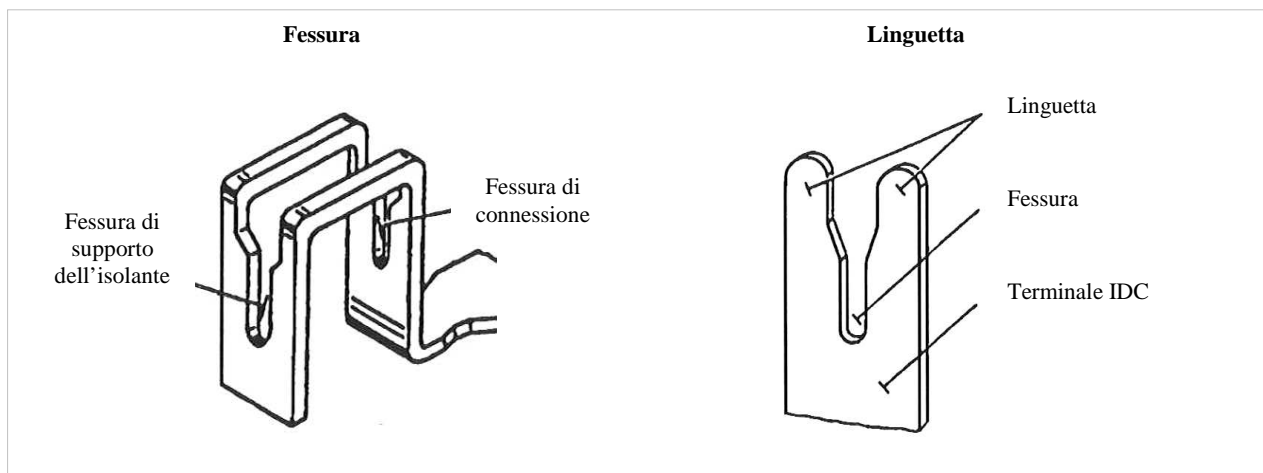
Illustrazione di una fessura di connessione e di una linguetta di un terminale IDC.
